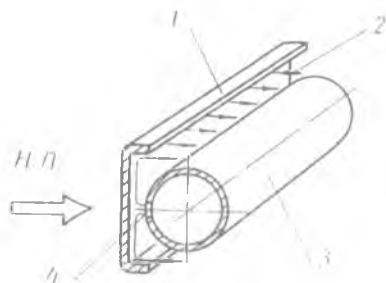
Струйный топливный коллектор с отбойной пластиной:
